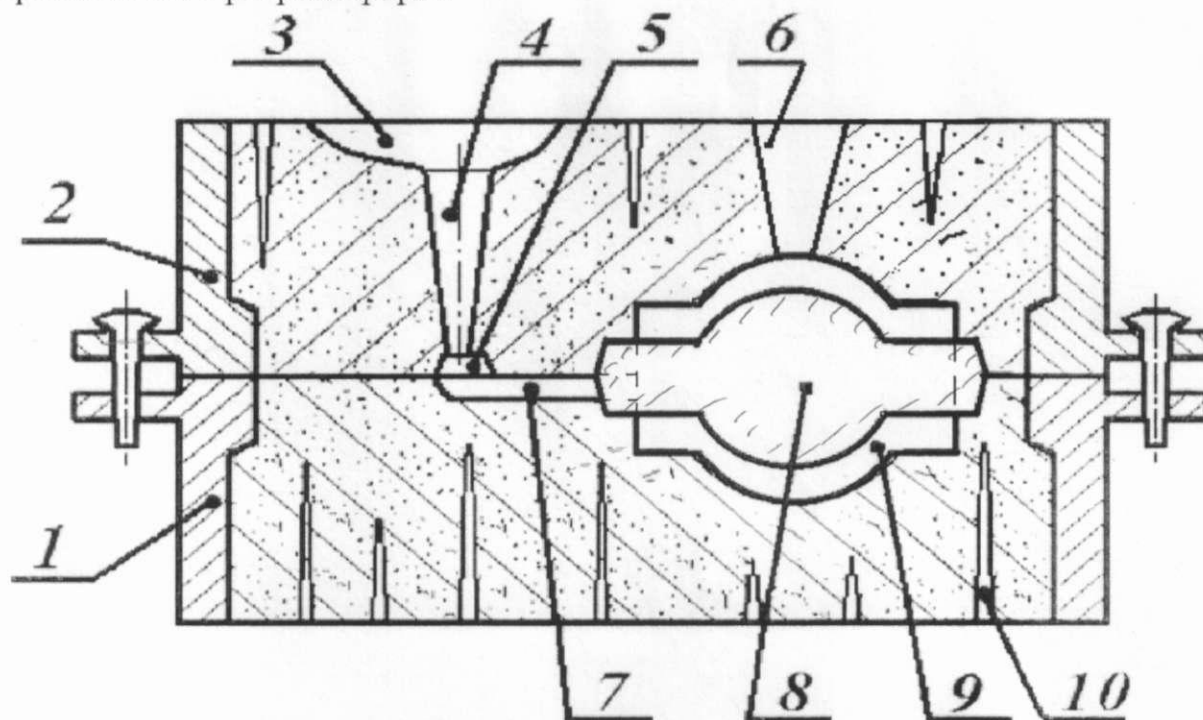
Эскиз разреза песчаной формы для отливки алюминиевого корпуса:
